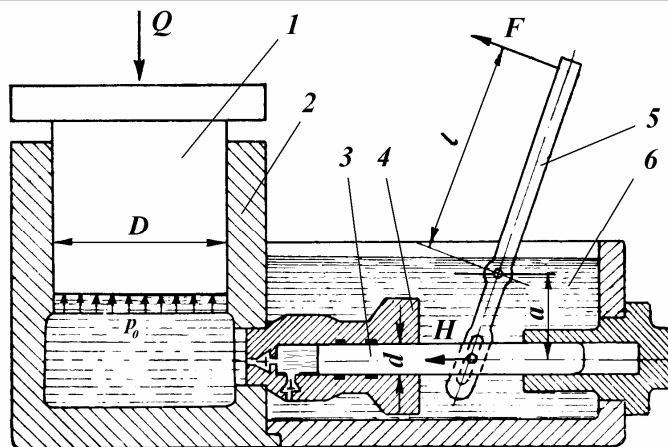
Cric hidraulic: 1- piston; 2- cilindru; 3- piston pompă; 4- cilindru pompă; 5- pârghie; 6- rezervor ulei.
